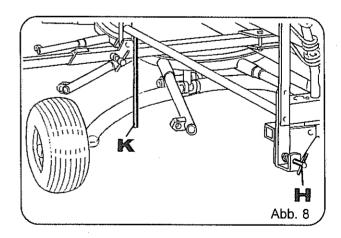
Abb. H = Sechskantschraube M 12 x 60 mit Mutter
